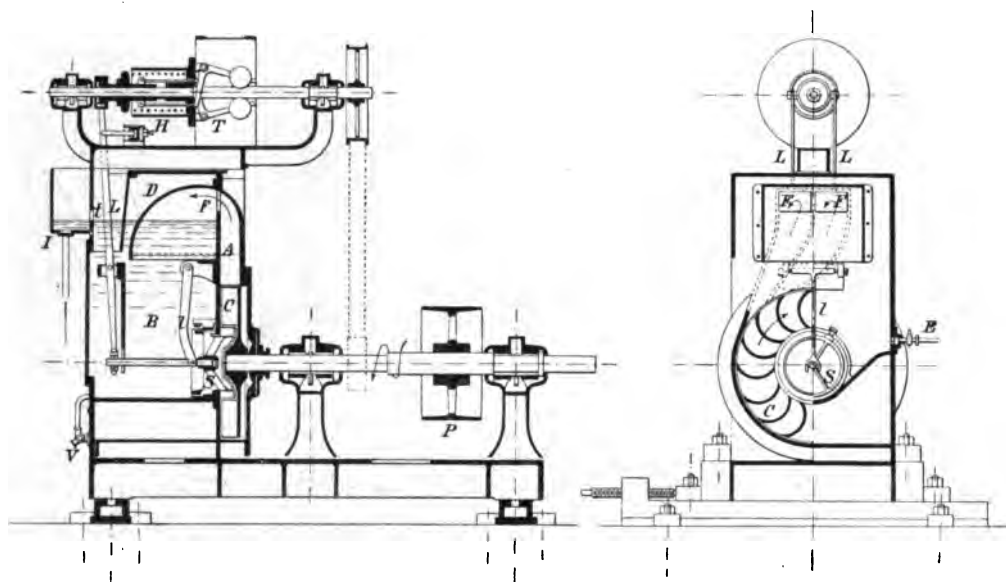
et 9. Régulateur Rusch Sendtner à résistance hydraulique.
